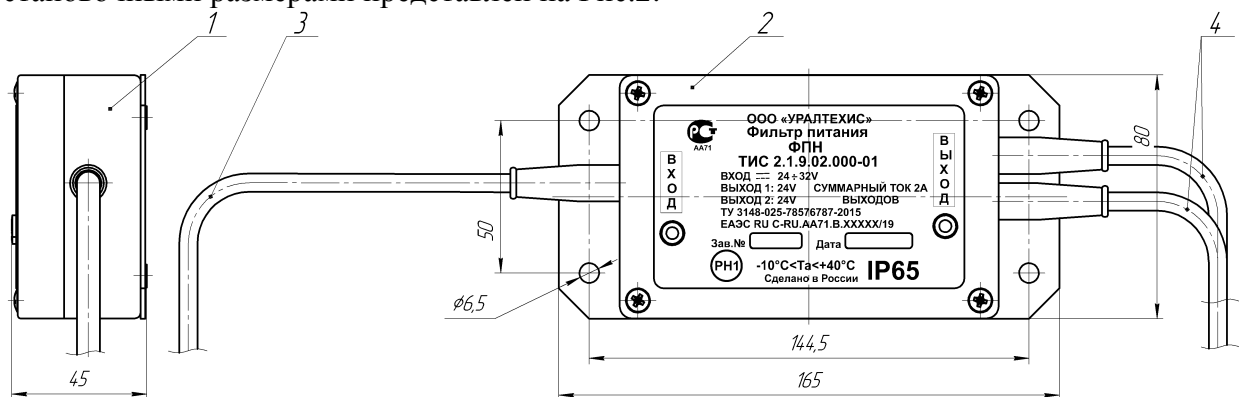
Внешний вид фильтр питания ФПН ТИС 2.1.9.02.000-01
